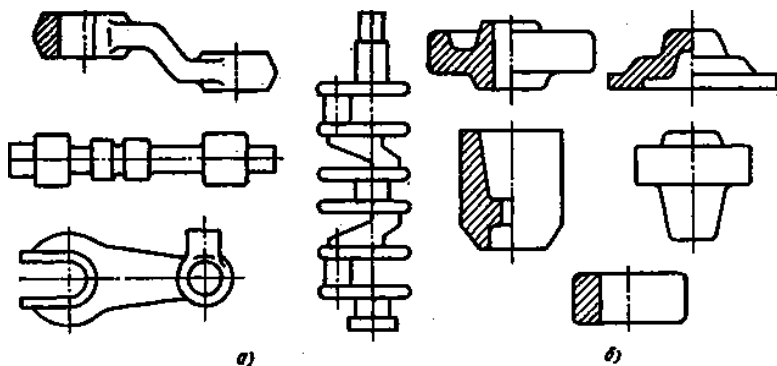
Штампованные поковки рычагов, коленчатого вала, заготовок изделий шестерен и др.
